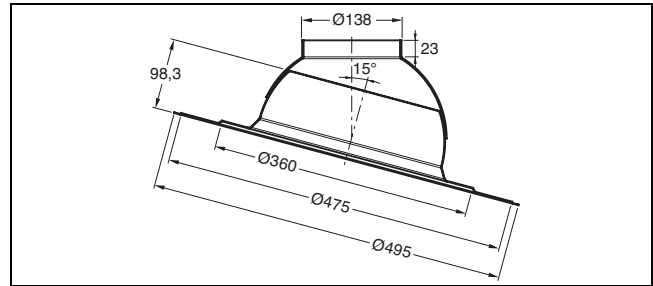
Flachdach-Klebeflansch (Maße in mm)
